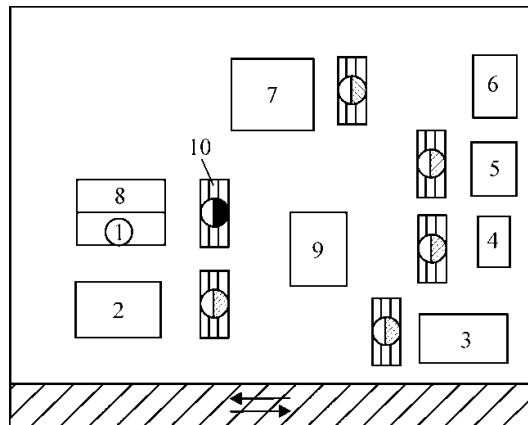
Робоче місце слюсаря з механо-складальних робіт (площа 28,7 м²): 1 – настільно-свердлильний верстат; 2 – верстак слюсарний; 3 – підставка-решітка; 4 – стіл для деталей; 5 – ванна пересувна; 6 – плита повірочна; 7 – прес рейковий; 8 – пристосування для редагування шатуна; 9 – стенд для гідровипробування; 10 – прес гідравлічний
